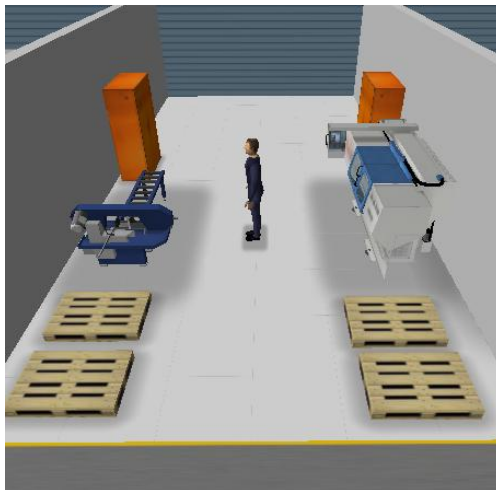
3D layout znázorňující první buňku, kde se vyrábí „Tělesa spojek“
